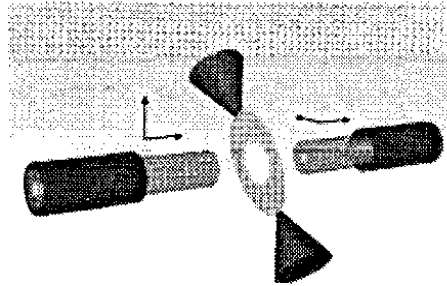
Принцип сварки электрической дугой
